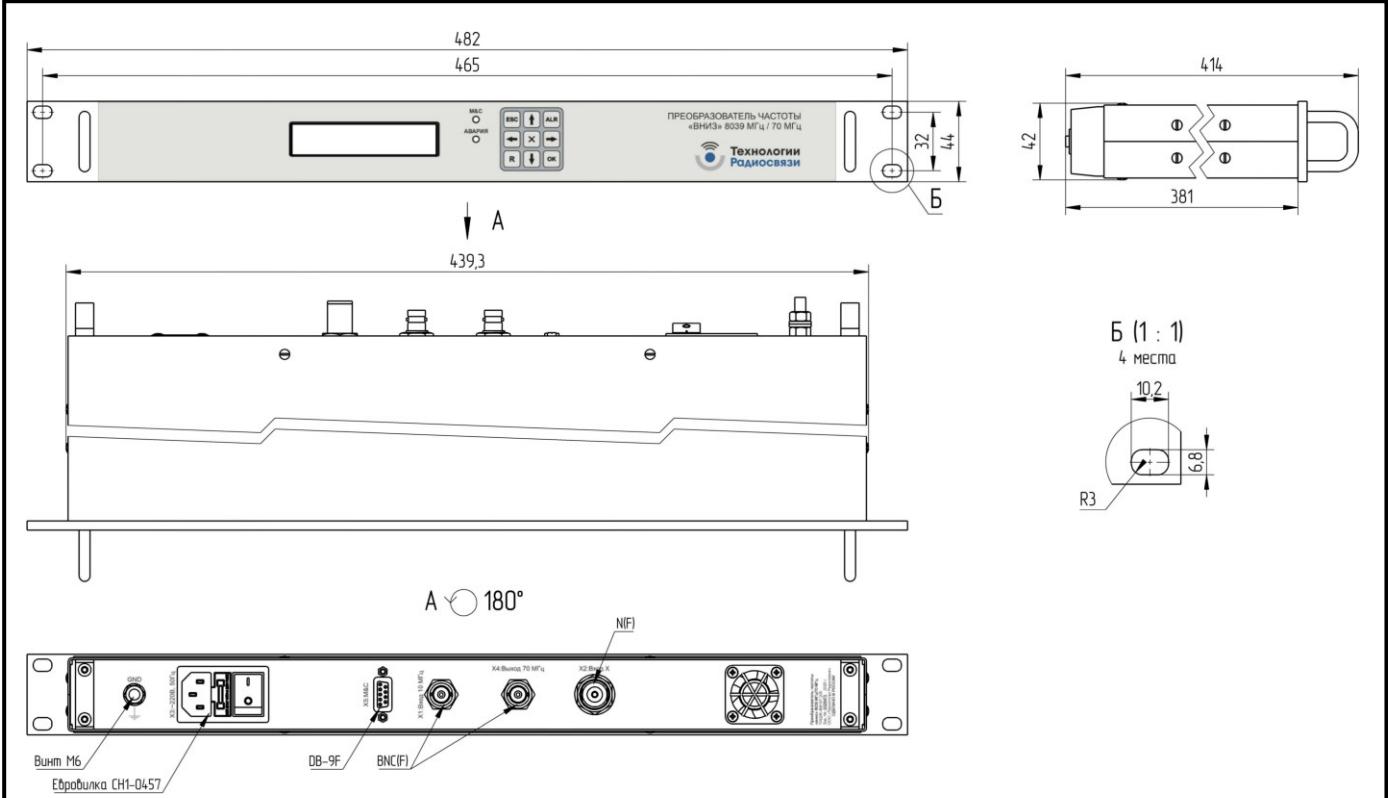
Габаритный чертеж ПЧ «вниз»
